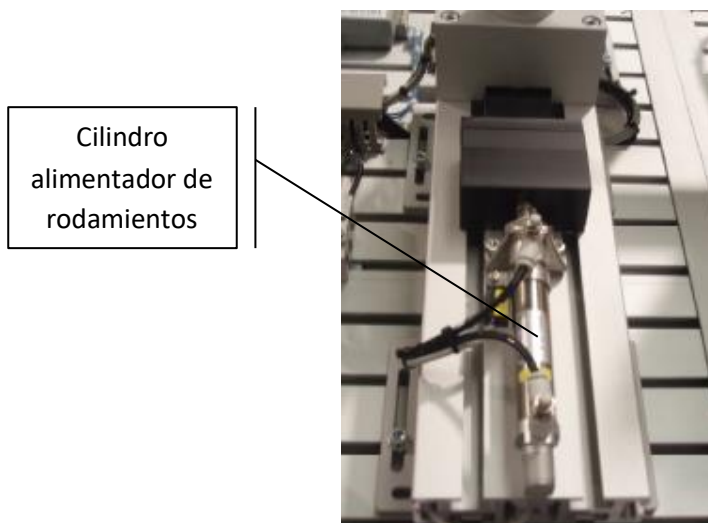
Alimentador de rodamientos. Fuente: (www.smc.eu).
